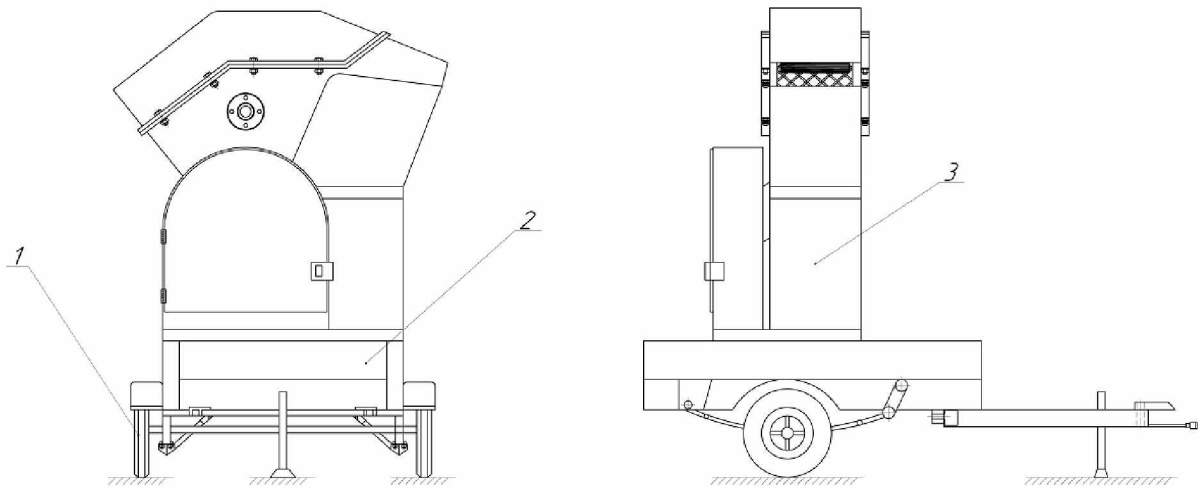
Общий вид мобильной установки для измельчения древесной зелени: 1 – колесная пара; 2 – сварная рама; 3 – отделяюще-измельчающая установка
